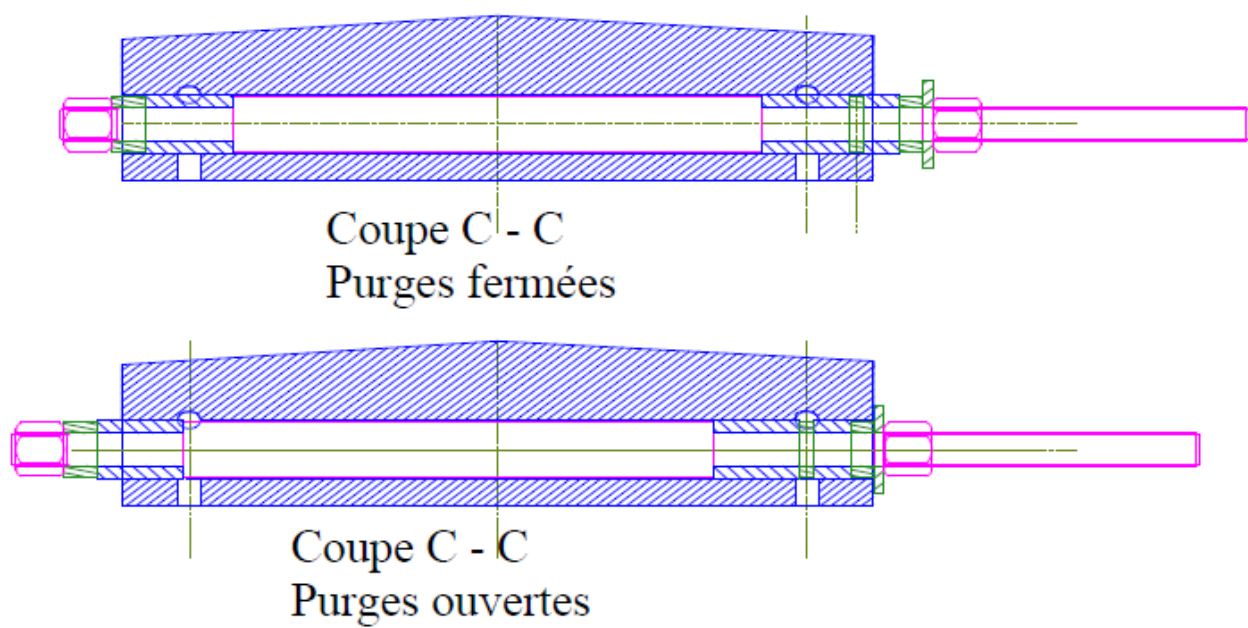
coupe CC – robinets de purges fermés et ouverts
